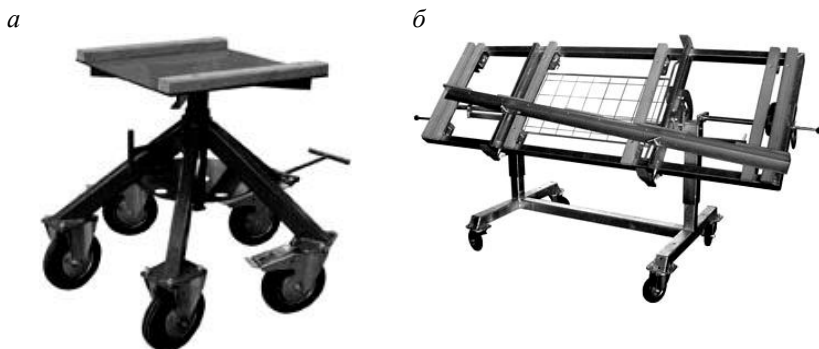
Рухомі поворотні столи для обробки каменю [2]
